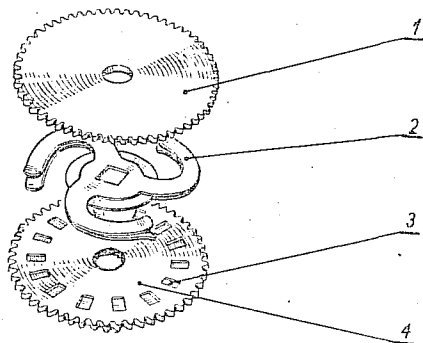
Wyłącznik w automacie „Etarotor 1216”.
